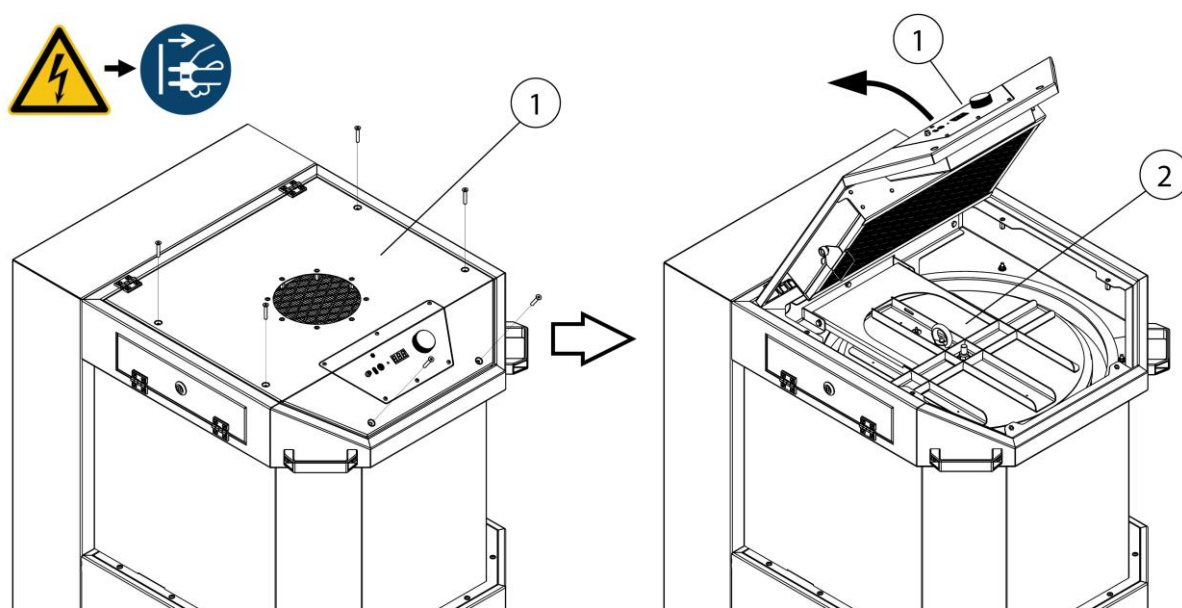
Remplacement du filtre – Accès à la cartouche filtrante
